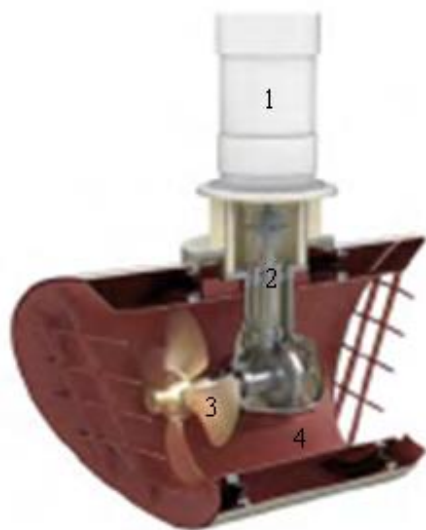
Подруливающее устройство: 1 – двигатель; 2 – редуктор; 3 – винт; 4 – труба
